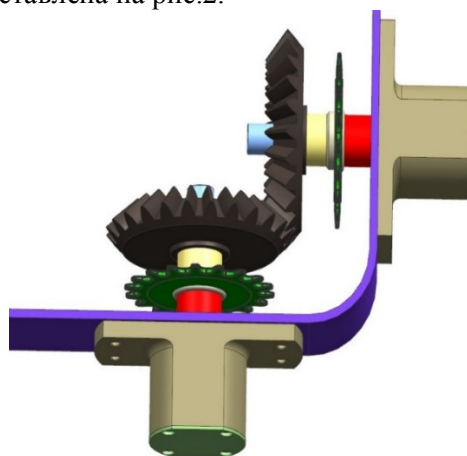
Цифровая модель конической зубчатой передачи смесителя
